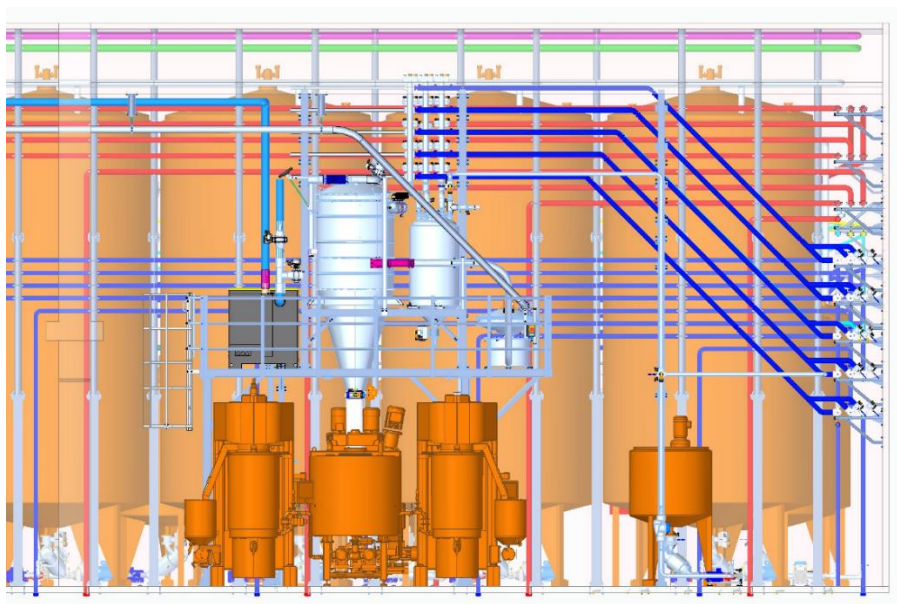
Vista frontale zona produzione creme bianche (Solid Edge)
